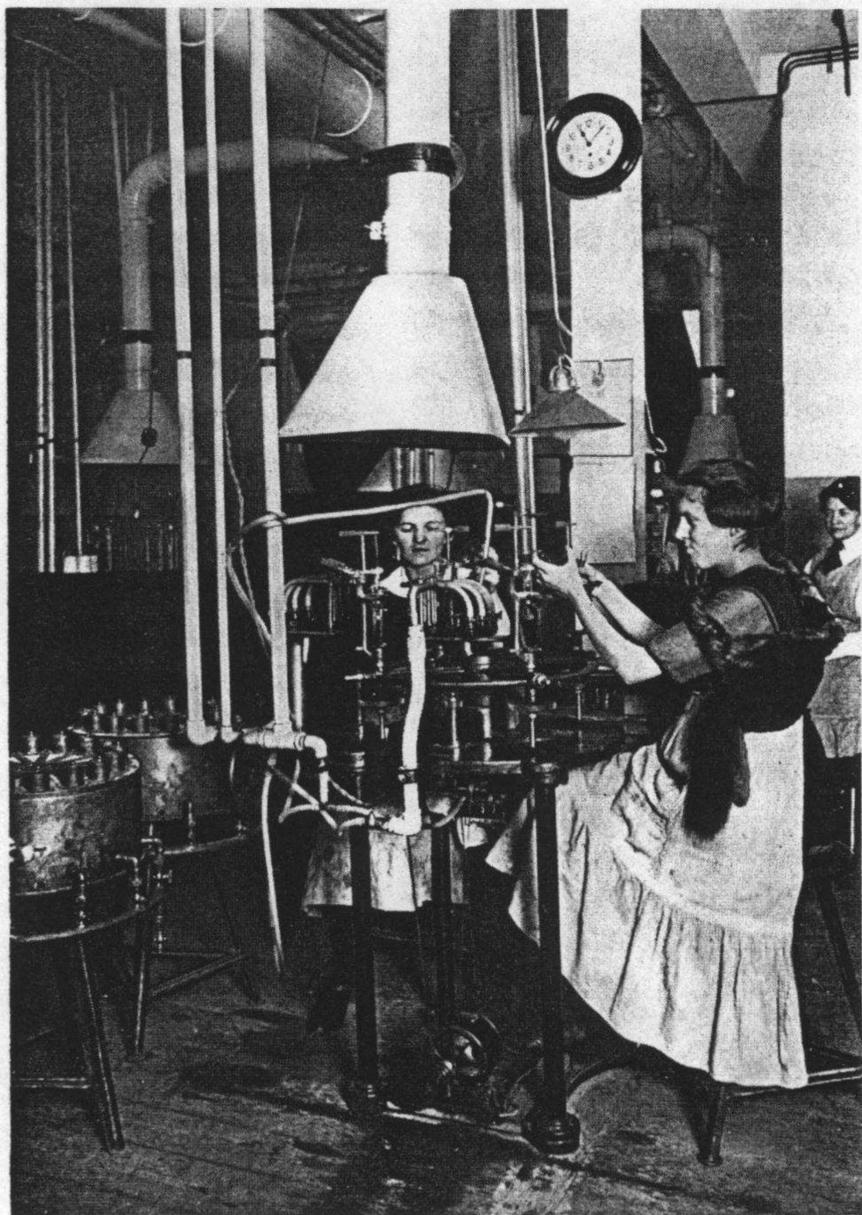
Quetschmaschine für Tellerfüße (TEGLA 1922)
